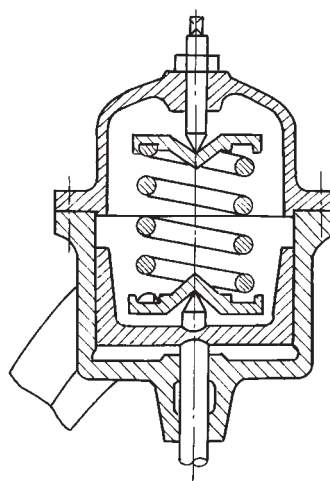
Установка пружины сжатия на шарнирных опорах
